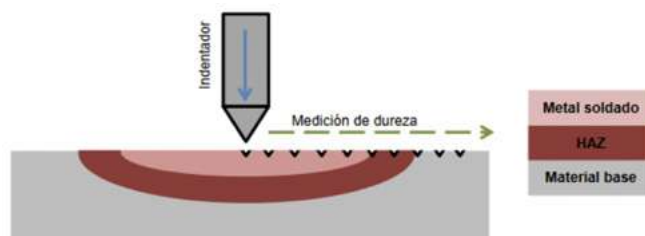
Esquema de prueba de dureza en la soldadura.
